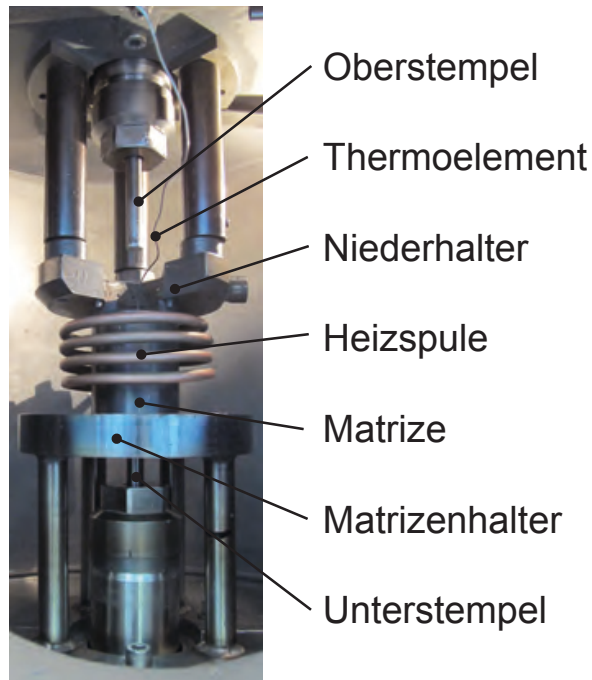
Aufbau der Werkzeuge in der Heißpresskammer
